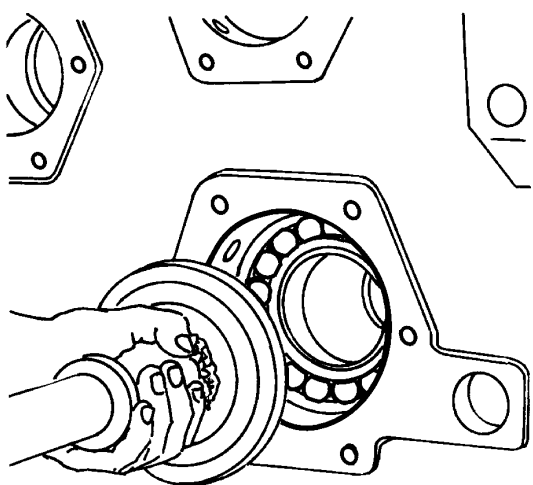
С.24. Подсадка бочкообразного подшипника (26)
